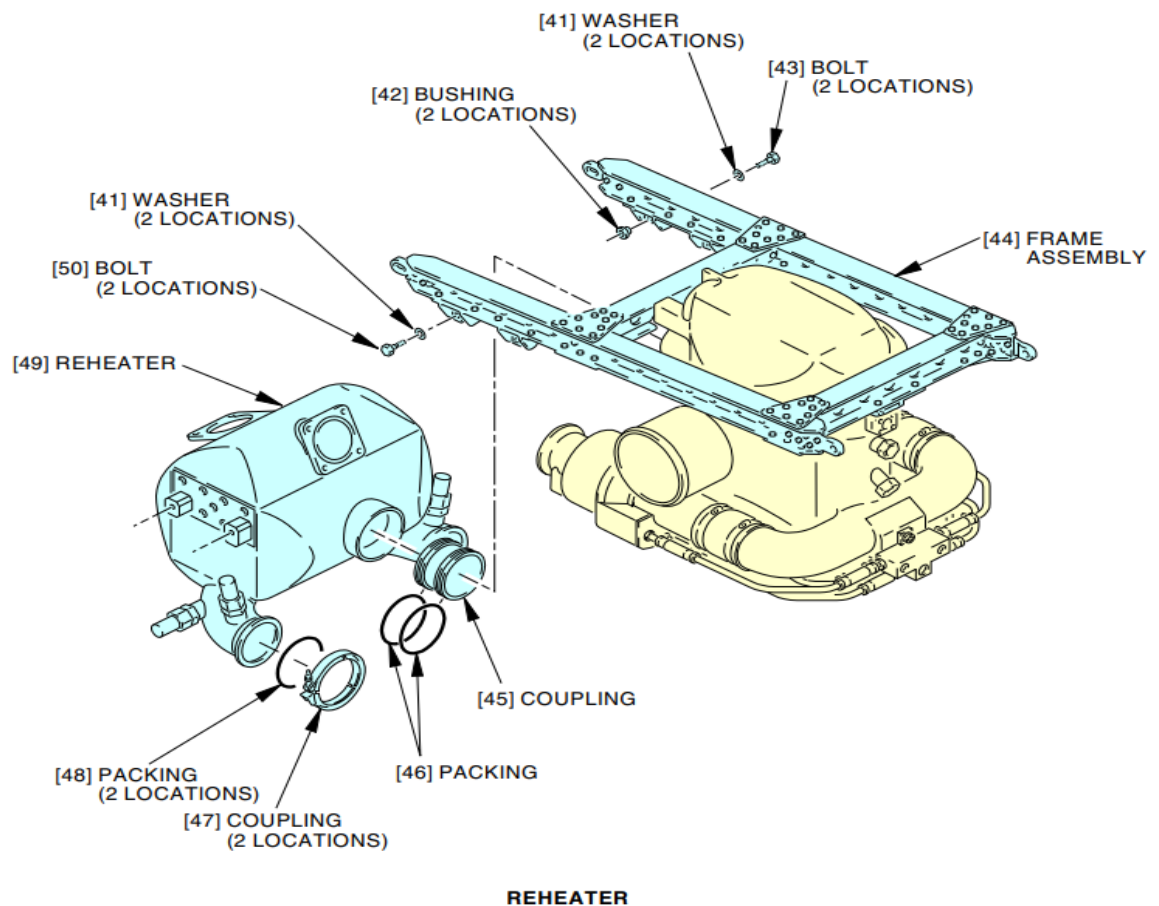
20 *Remove reheater from the frame assembly* (sumber: dokumentasi pribadi)
